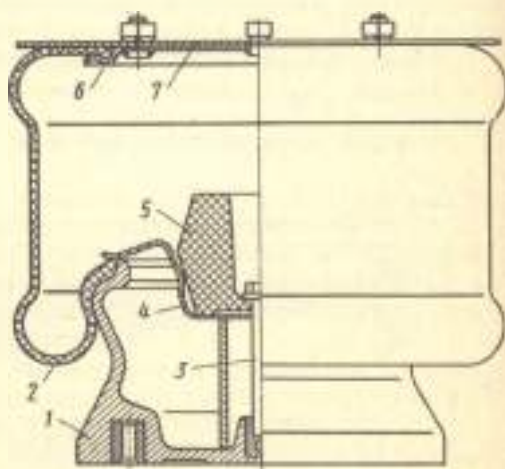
Конструкция пневмобаллона рессоры: 1 — поршень; 2 — кожа; 3 — болт; 4 — стопорный стакан; 5 — резиновая подушка; 6 — запирающая крышка; 7 — покрывная пластина
